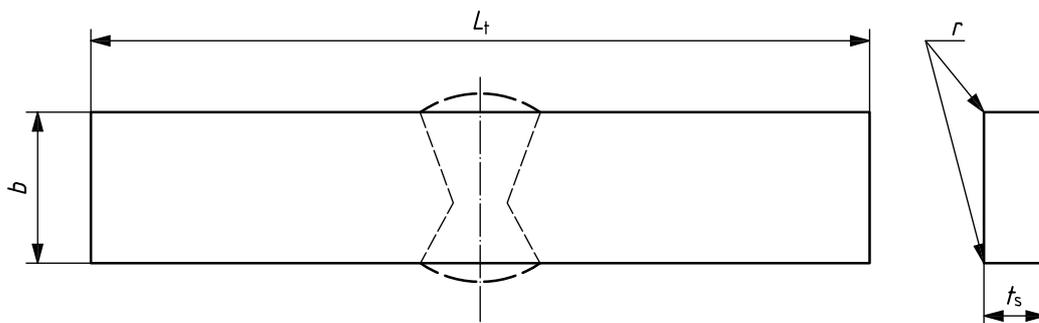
Éprouvette de pliage transversal de côté sur soudure bout à bout (SBB)
